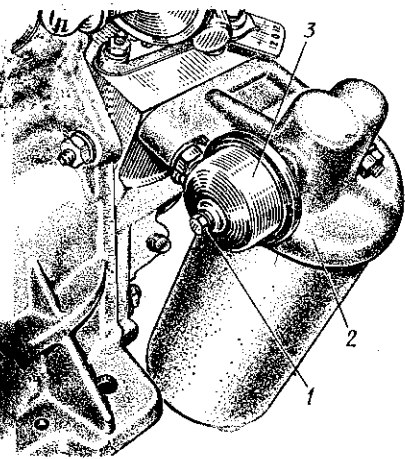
Расположение датчика указателя давления масла: 1 — винт присоединения провода; 2 — крышка корпуса фильтра; 3 — датчик указателя давления масла
